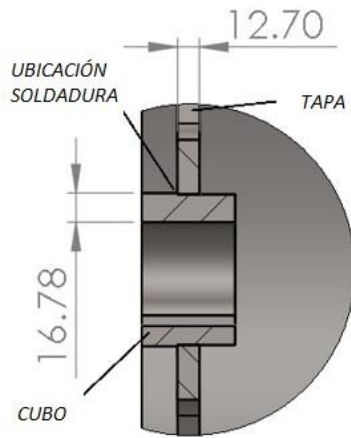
Ubicación soldadura N° 1
